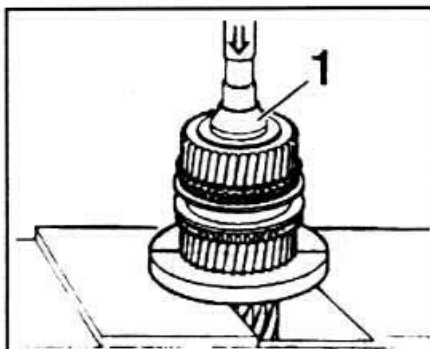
Выпрессовка промежуточного вала из блока шестерен с помощью приспособления BMW 23 2310 с упором на шестерню III передачи:
